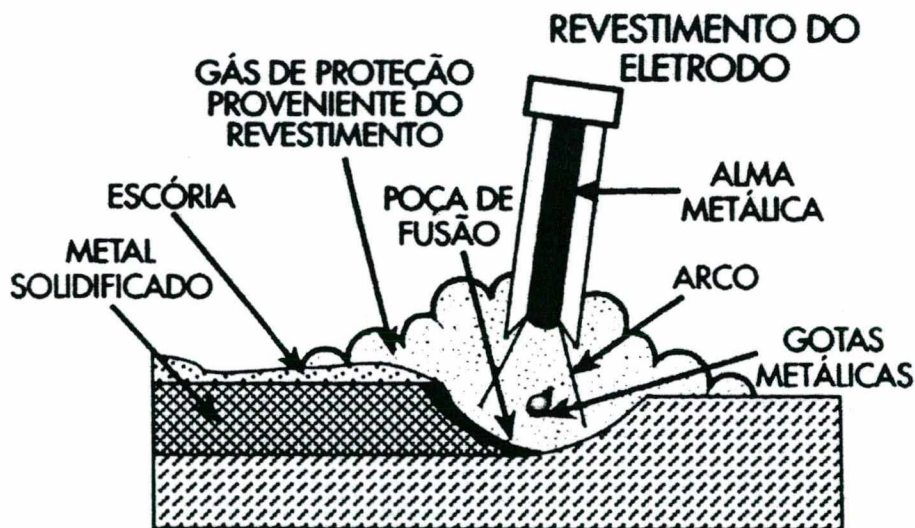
Soldagem a Arco Voltaico com Eletrodo Revestido (SMAW).
